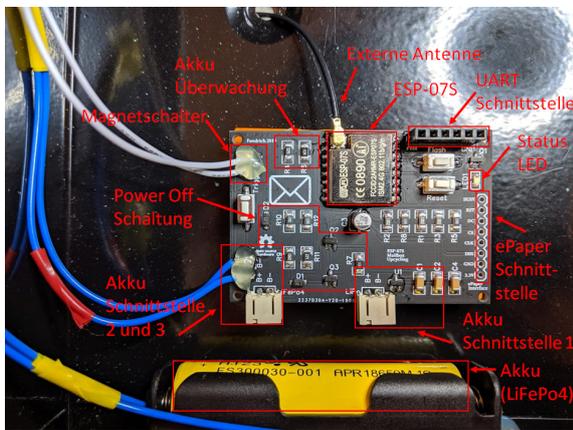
Platine, Kabel zum Magnetschalter und Akku im Briefkasten.
